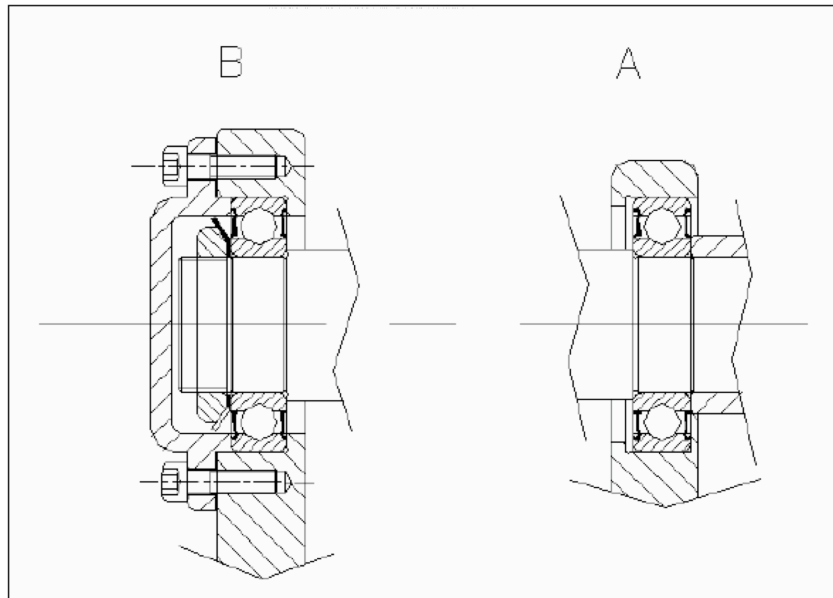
Dettagli del sistema di fissaggio del cuscinetto A ed B
